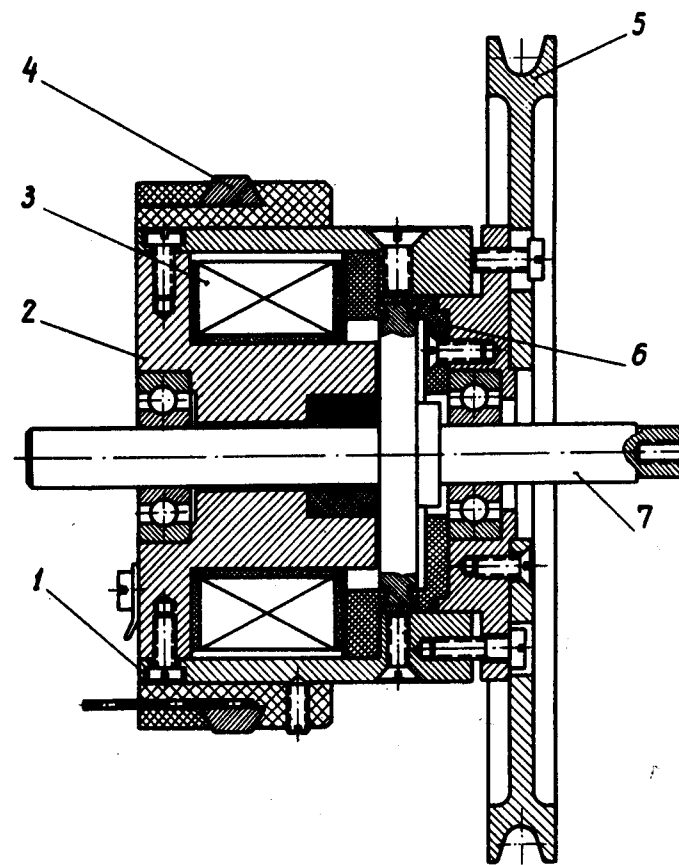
а. Муфта. 1 - корпус, 2 - сердечник, 3 - катушка,
